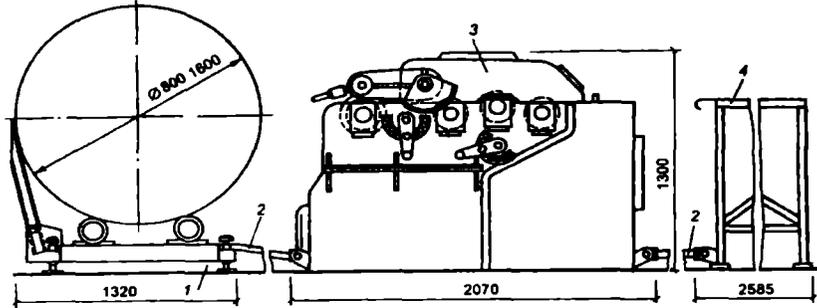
Установка конструкции ЦНИИОМТП для размотки, правки и резки рулонных сеток:
